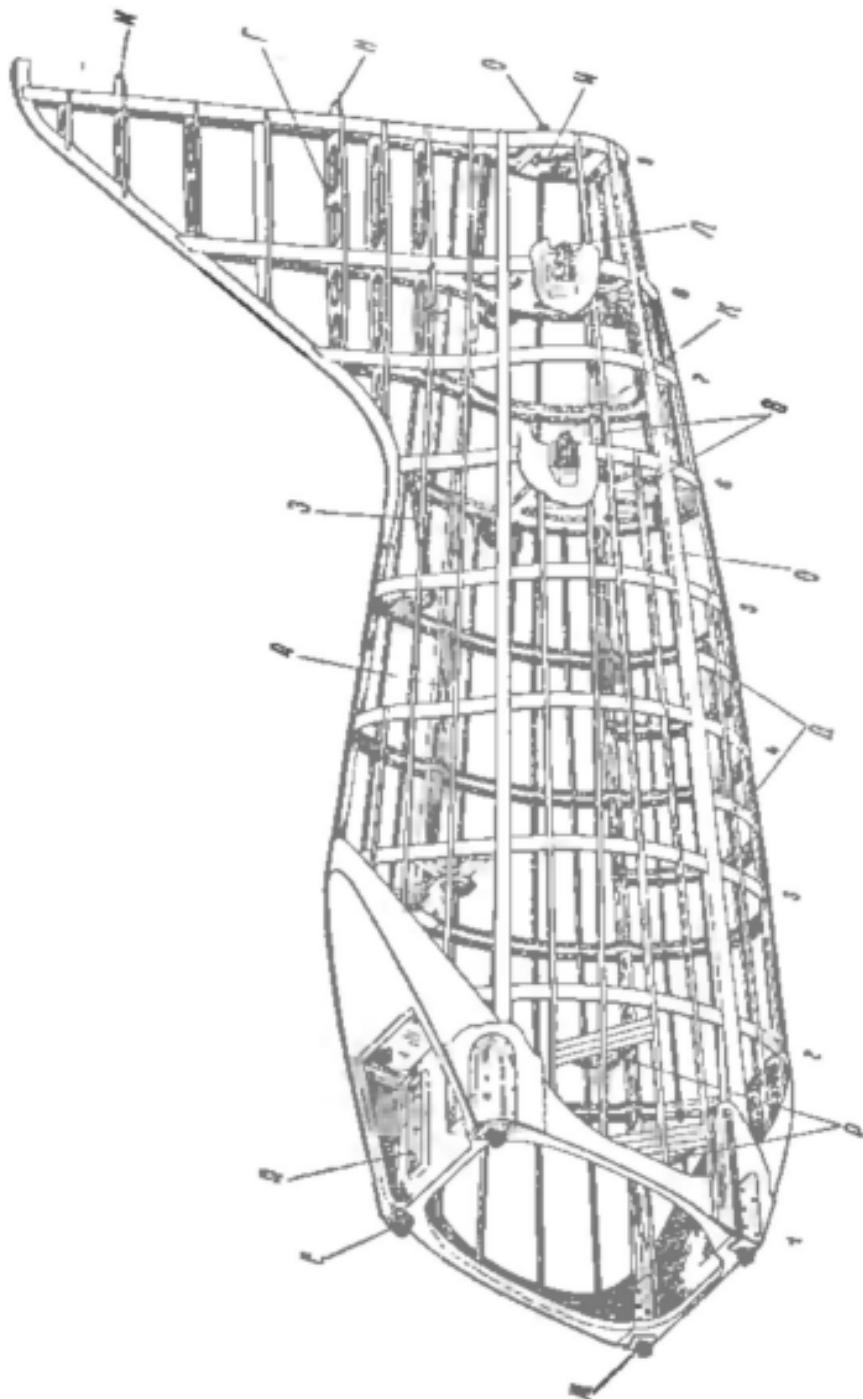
Верхний стыковой узел хвостовой части фюзеляжа.
